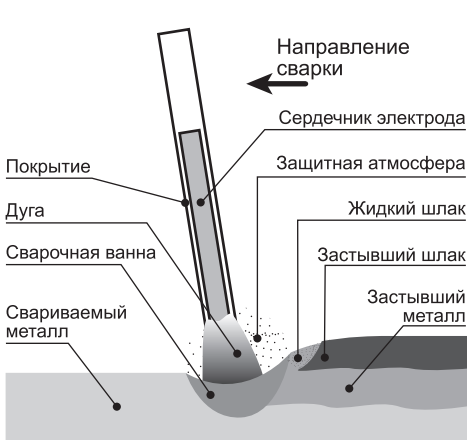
Схема процесса ручной дуговой сварки штучным плавящимся электродом
